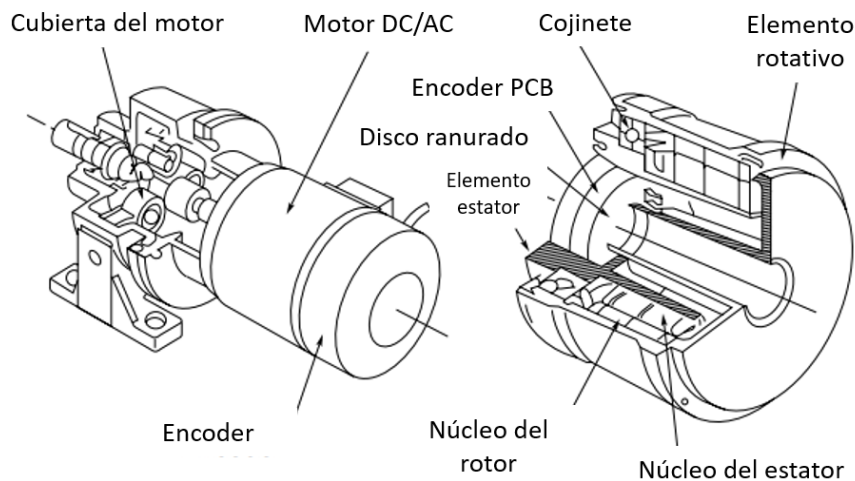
Motor con engranaje vs motor transmisión directa[5]
